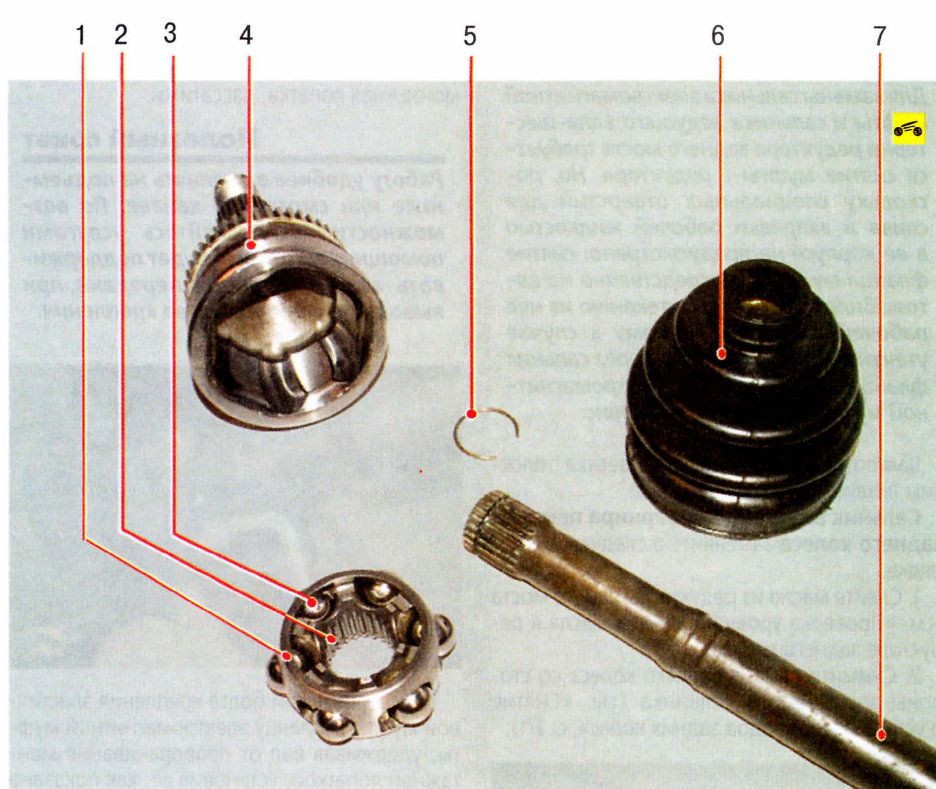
Детали наружного шарнира привода заднего колеса: 1 — сепаратор; 2 — обойма; 3 — шарики; 4 — корпус шарнира; 5 — стопорное кольцо; 6 — чехол; 7 — вал привода
